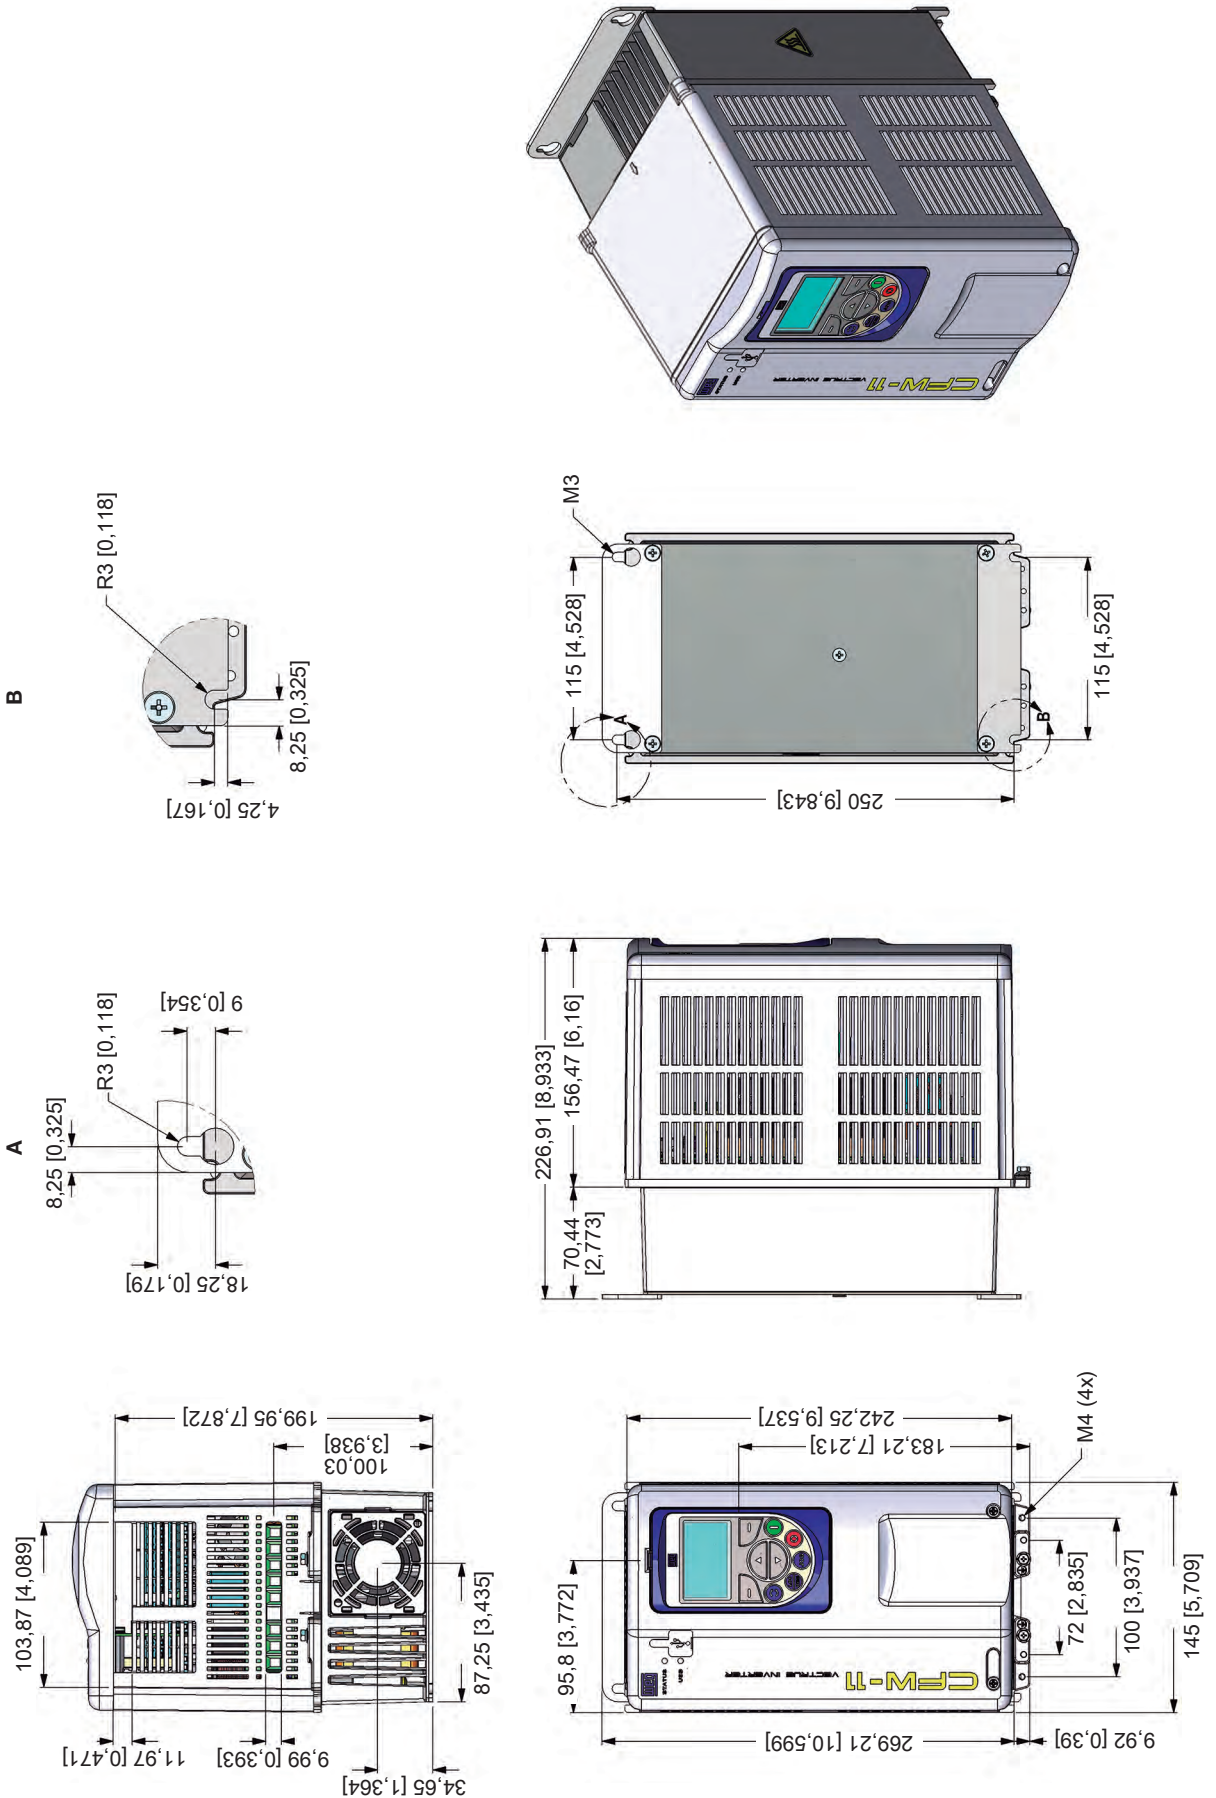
Габаритные размеры преобразователя, размер корпуса A, мм [дюйм.]
